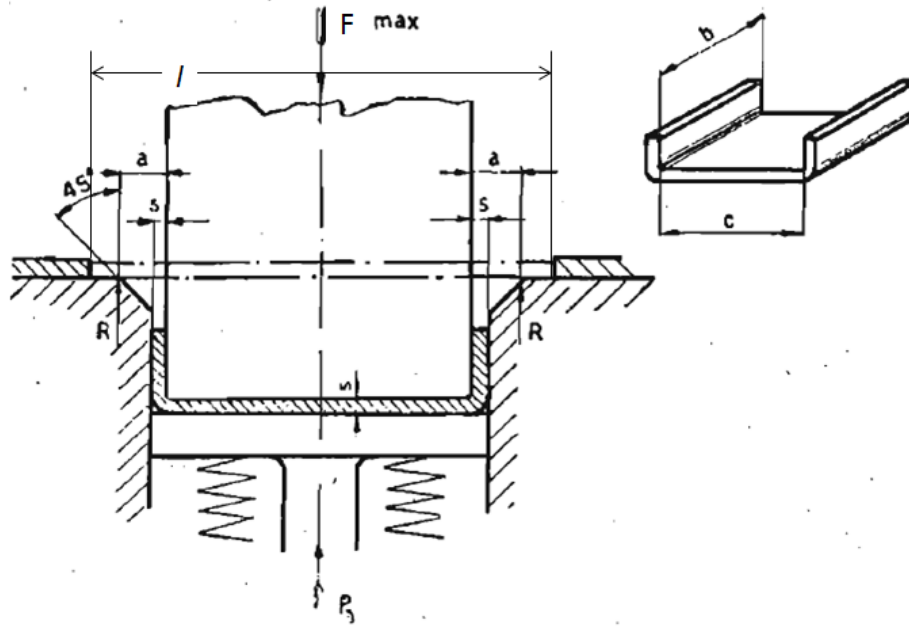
Dimensiones a tomar en cuenta en el doblado
